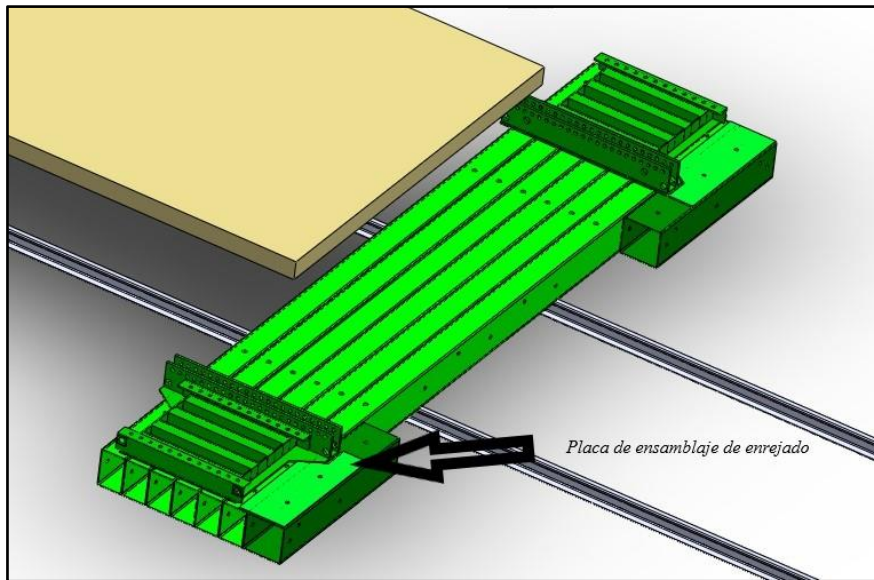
Ensamblaje enrejado superior. Fuente: Diseño propio.
